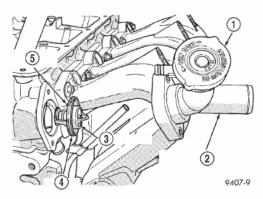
Conector de salida del motor y termostato motor 2.0L
